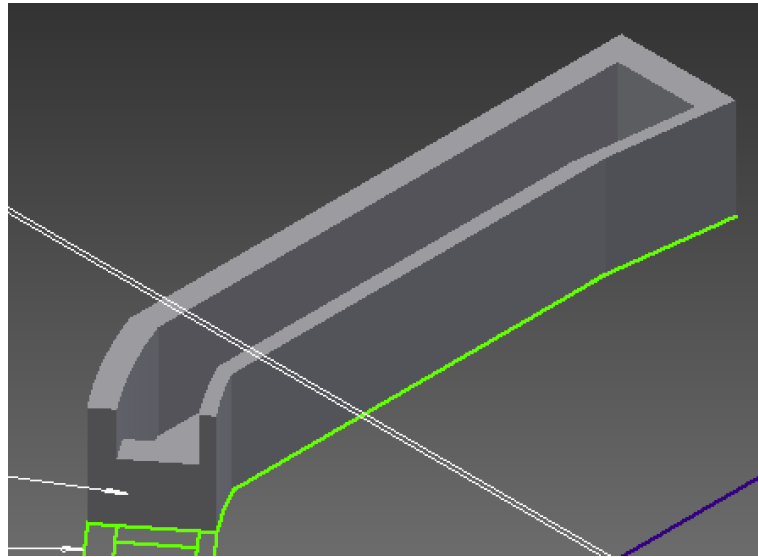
Vista frontal lateral izquierda desde arriba de pieza del lado izquierdo.
